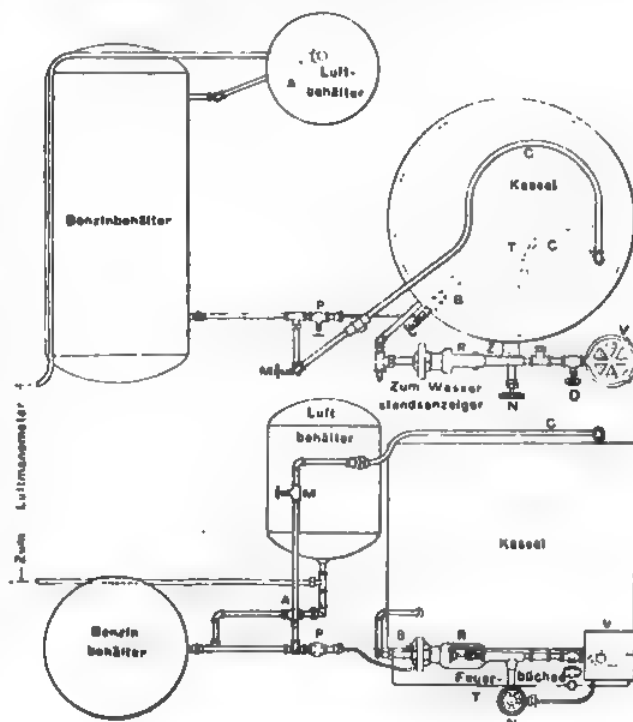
Readingwagen, Schema der Benzinzuleitung. (Oben Grundriss, unten Seitenansicht.)
